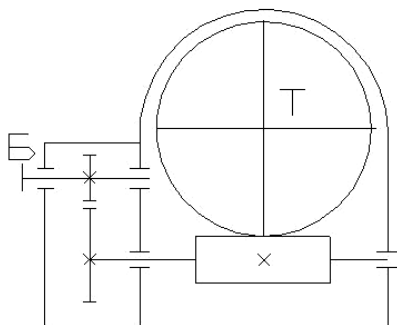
Двухступенчатый зубчато-червячный редуктор
